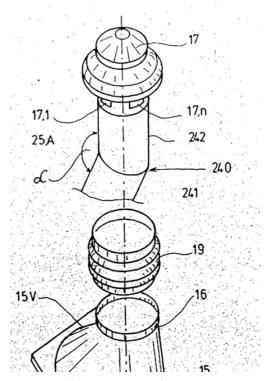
Фрагмент вытяжной кровельной вентиляции с колпачком головки вентиляционной трубы
